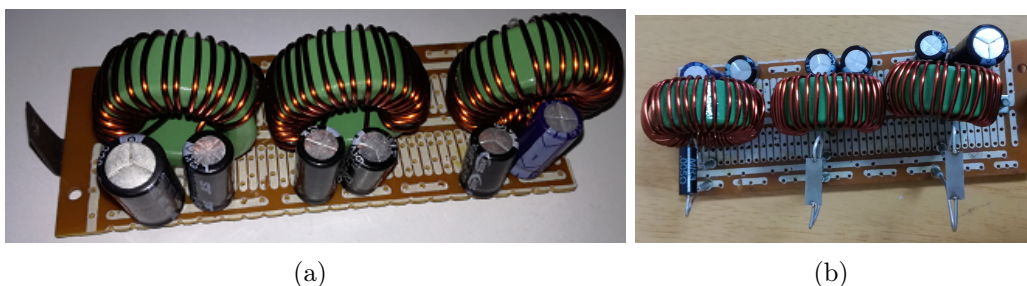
Circuito filtro de armónicos sobre PCB.
